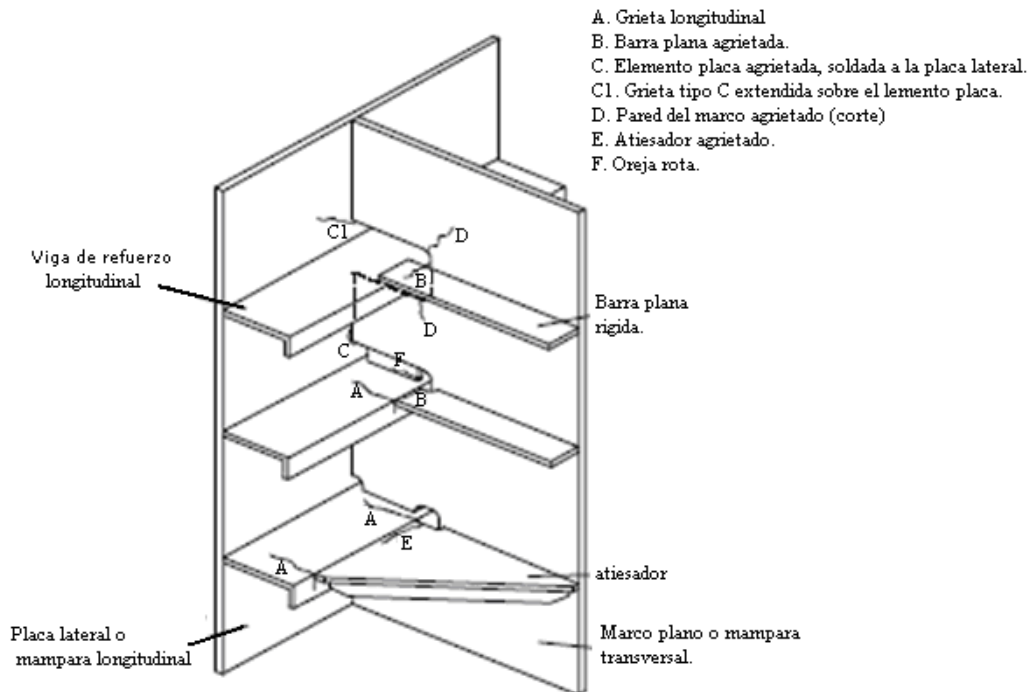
Tipos de grietas en elementos soldados. Ref. [26]
